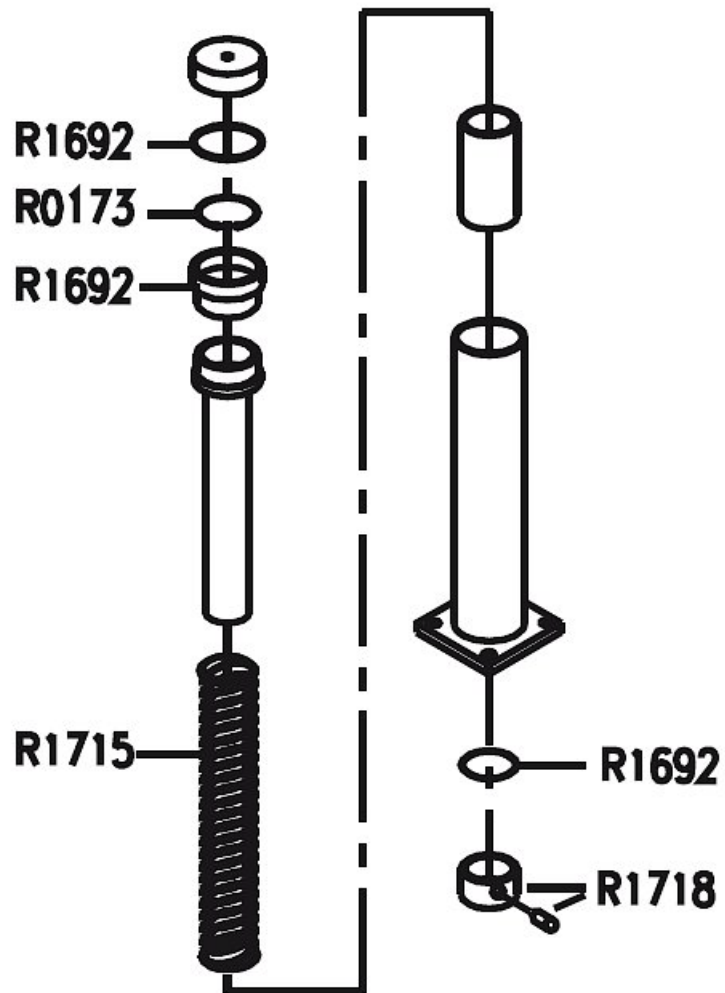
Ersatzteilzeichnung 3 - Zylinder
